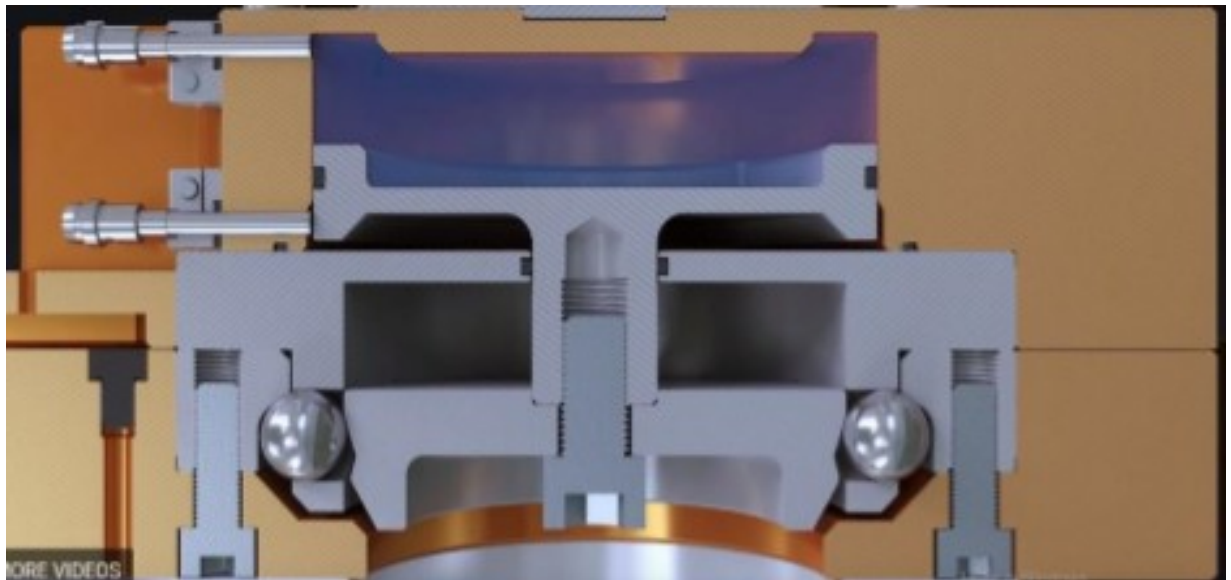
Пневматичний циліндр, що просувається до другої частини зміни інструменту
